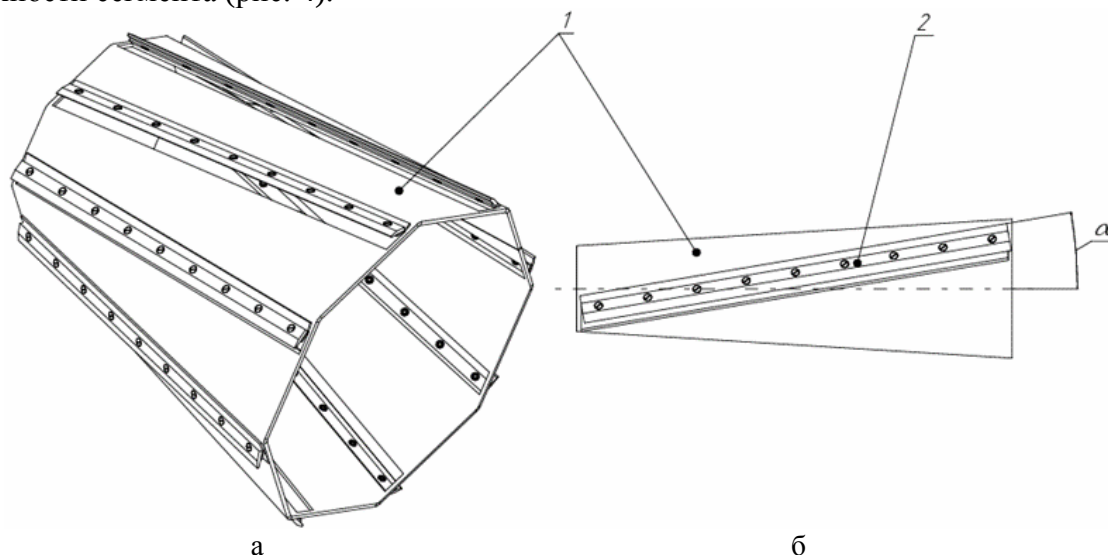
Угол расположения ножа α на поверхности сегмента 1 фрезерного барабана: а) полый конический фрезерный барабан; б) сегмент 1 фрезерного барабана с проходным ножом 2
